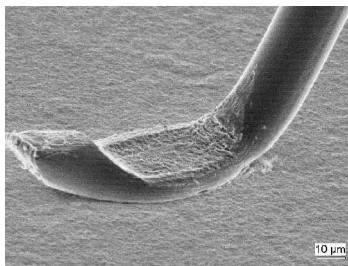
Внешний вид сварного соединения алюминиевой проволокой диаметром 30 мкм
